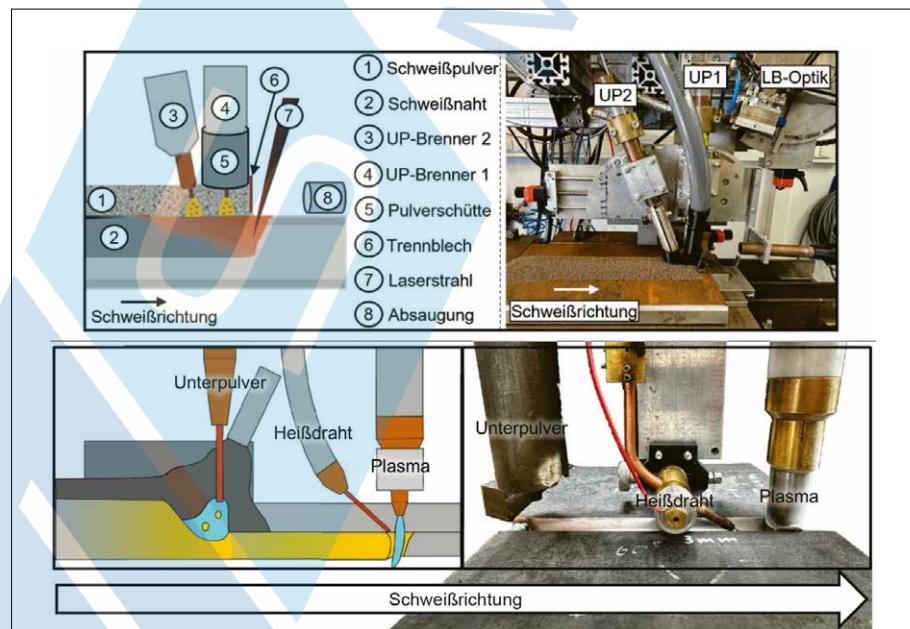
Laserstrahl-Tandemunterpulver-Hybridschweißprozess (oben) sowie Plasma-Heißdraht-Unterpulverschweißen (unten; Prinzip jeweils links, realer Versuchsaufbau jeweils rechts).
